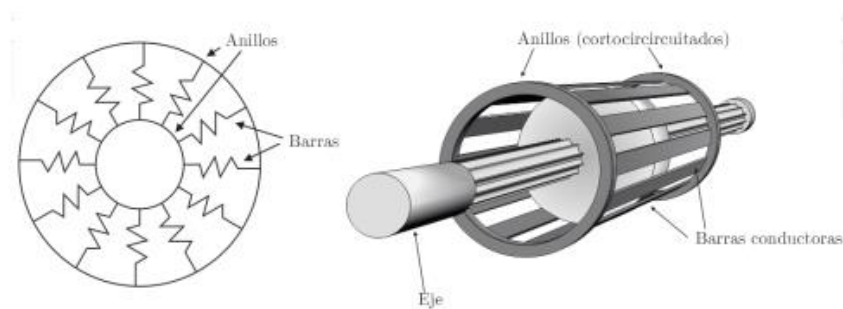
Rotor bobinado Jaula de Ardilla Simple [35].
